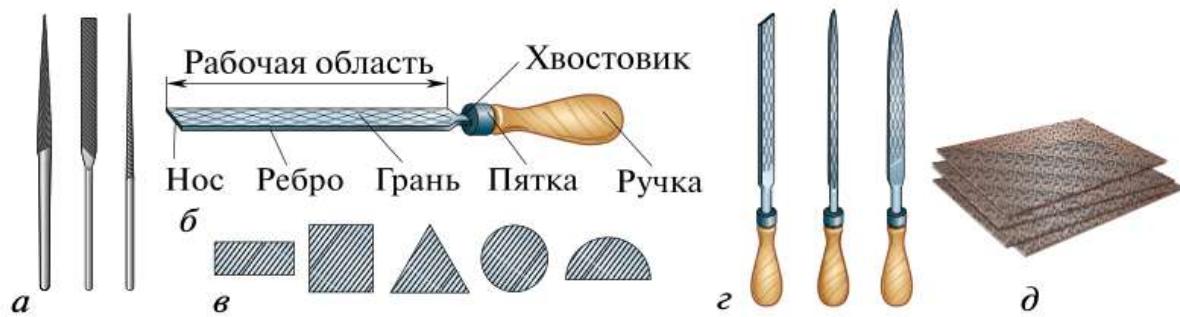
Инструменты для зачистки, чистовой обработки и шлифовки заготовок из древесины: *а* — надфили; *б* — основные части напильника; *в* — формы сечения напильников; *г* — рашпили; *д* — шлифовальная шкурка
